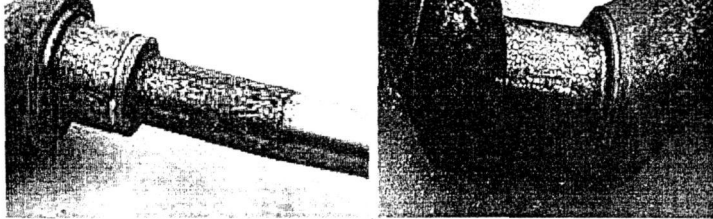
Рабочая поверхность коленчатого вала с нанесенным твердым сплавом
